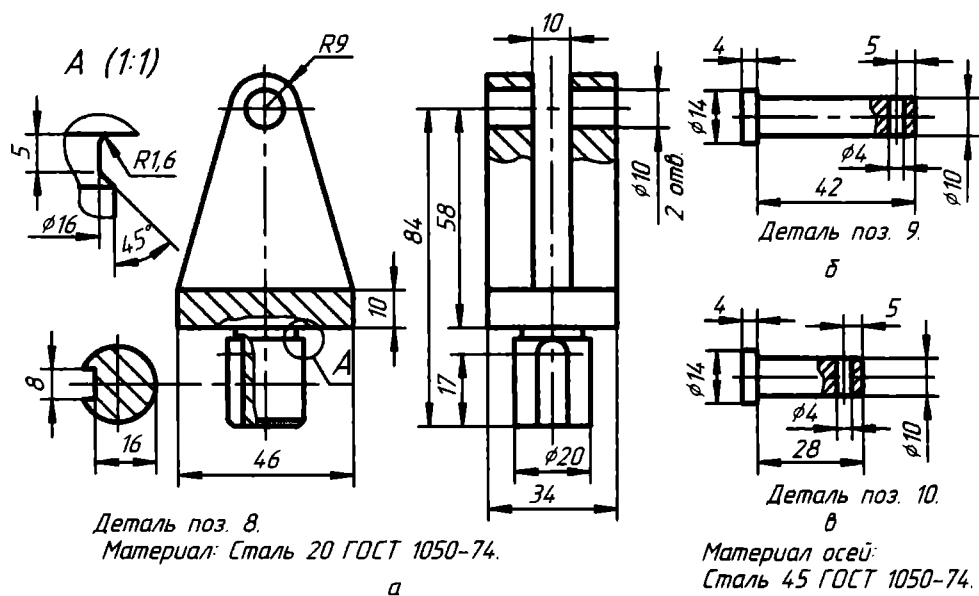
Чертежи: а — стойки; б, в — осей
